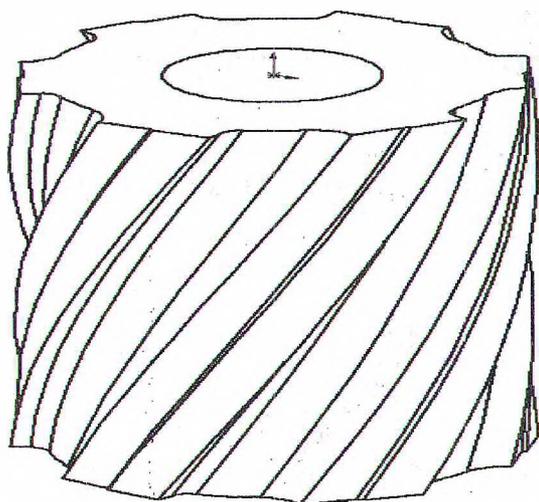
Фреза с неперетачиваемыми твердосплавными пластинами
